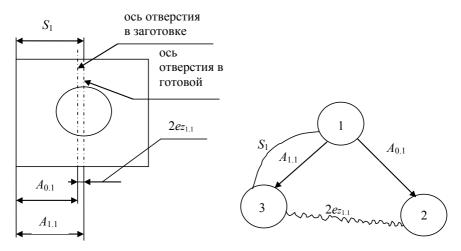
Схема обработки и граф размерных связей для детали с отверстием
